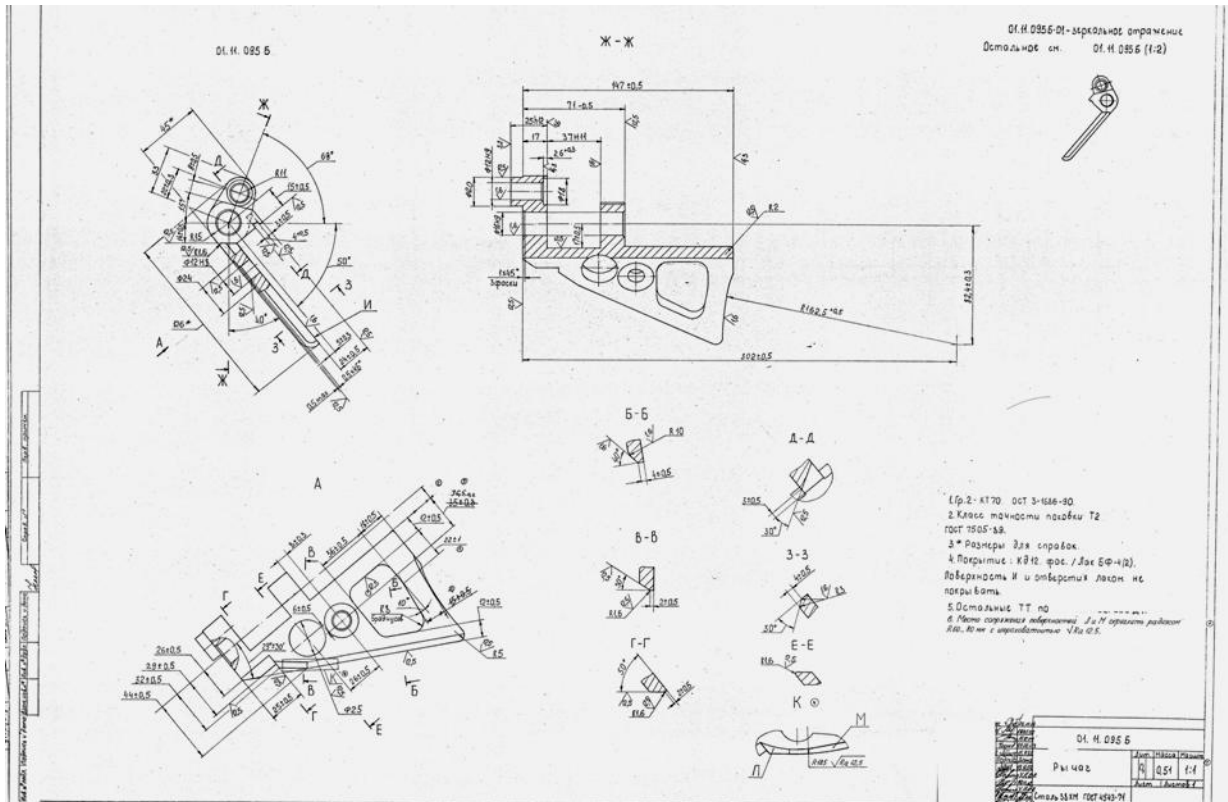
Технический многовидовый чертёж детали «Рычаг_1»
